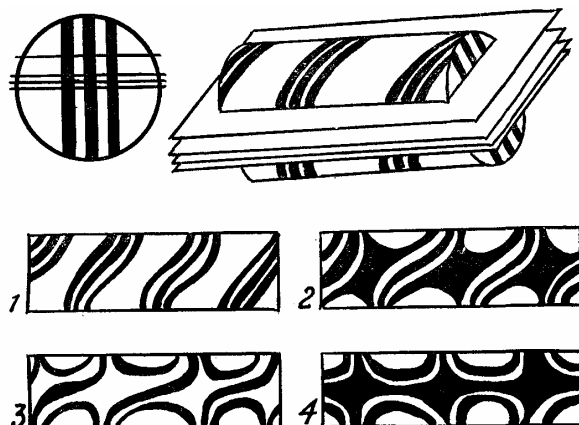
Схема получения узоров сварочного булата на модели блока из трех пластин.
